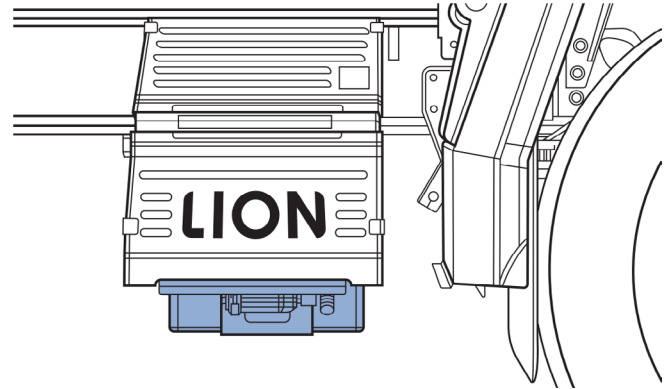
Emplacement du réservoir de diesel pour le chauffage à combustible
